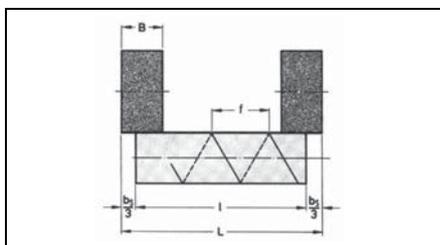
Наружное круглое шлифование с продольной подачей
